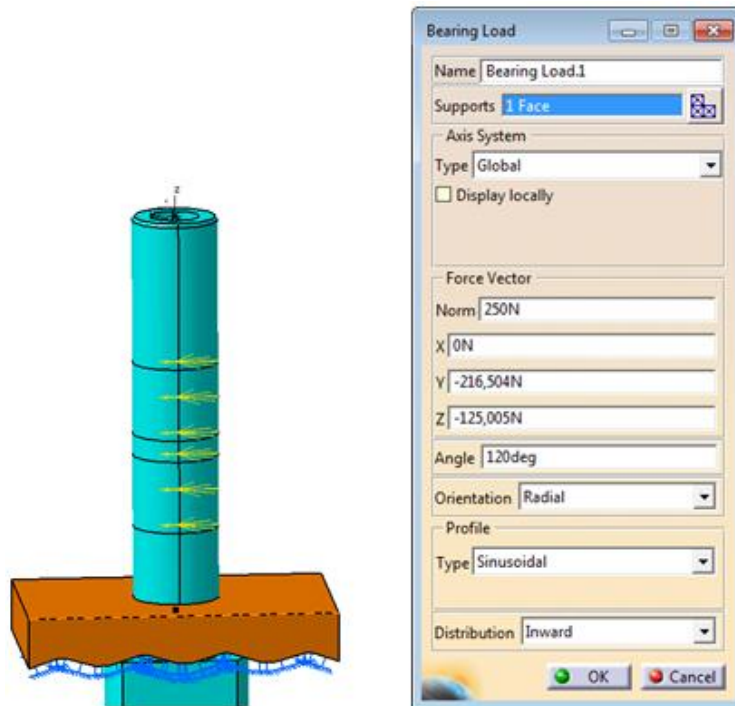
Detalle de la aplicación de las cargas distribuidas sobre el eje.
